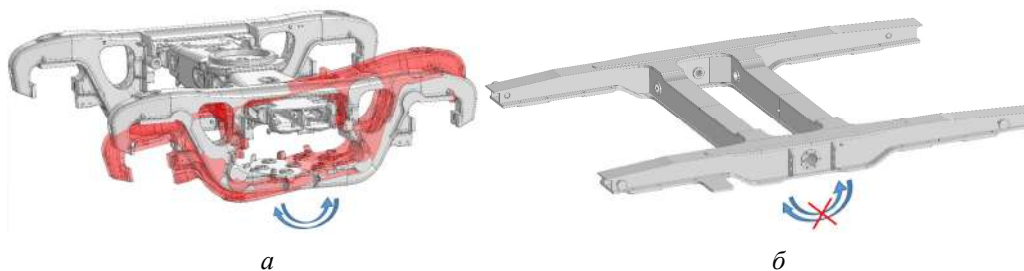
Схематизированное представление восприимчивости несущих конструкций тележек к кососимметричным нагрузкам: *а* – сочленение несущих конструкций тележки типа 18-100; *б* – рама тележки жесткой сварной конструкции
